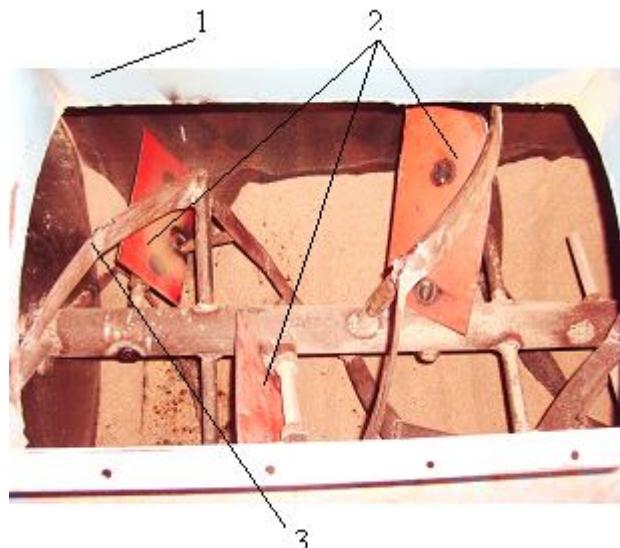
Робочий орган змішувача: 1 – корпус змішувача; 2 – лопатки;
